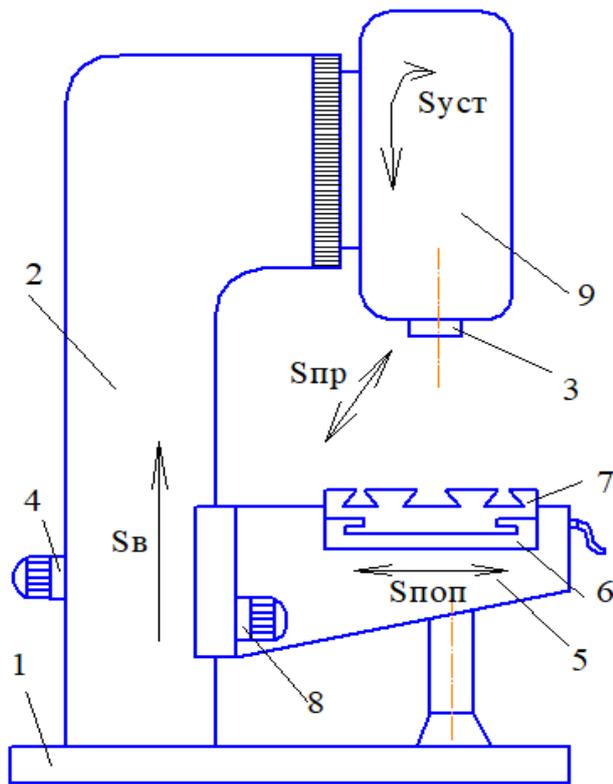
Компоновка консольного вертикально-фрезерного станка
